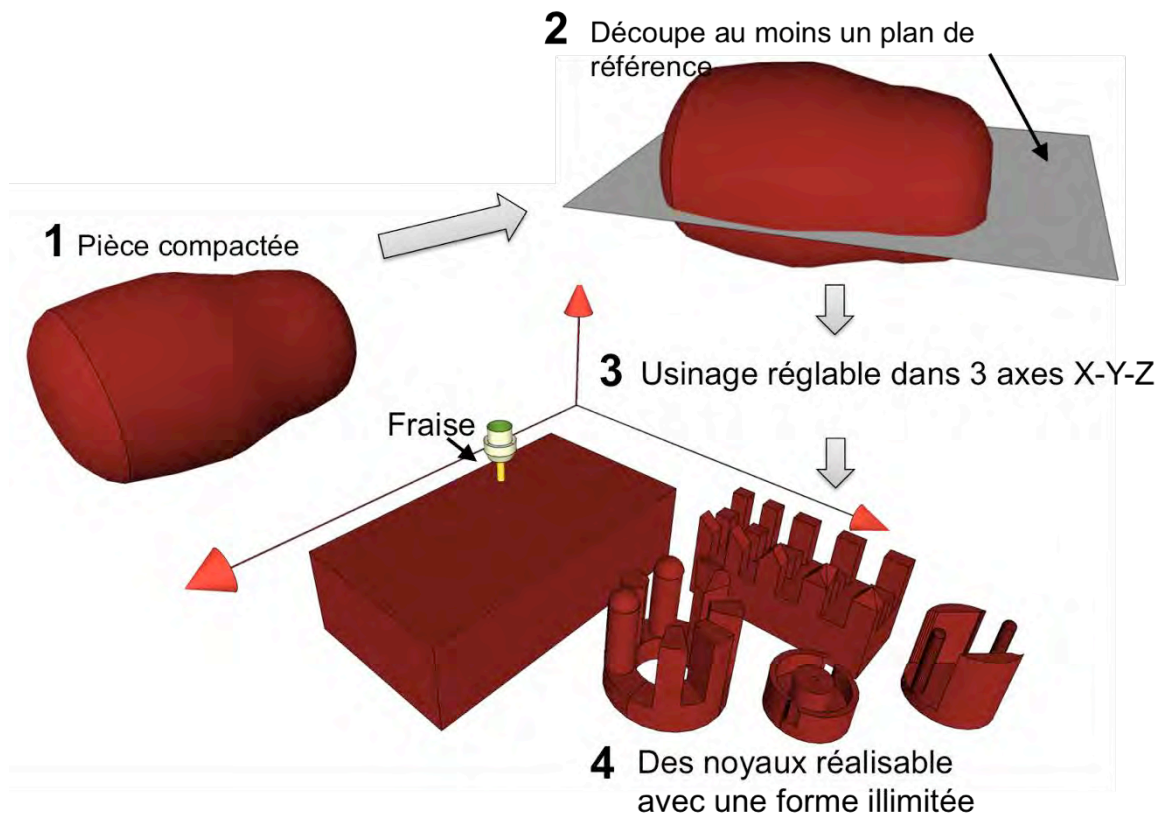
Etape d'usinage d'une pièce compactée avec des formes usinables par un fraisage numérique 3D
